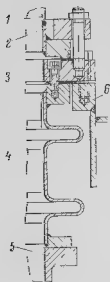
Соединение патрубка обшивки ЦНД и ресивера с корпусом ЦНД
